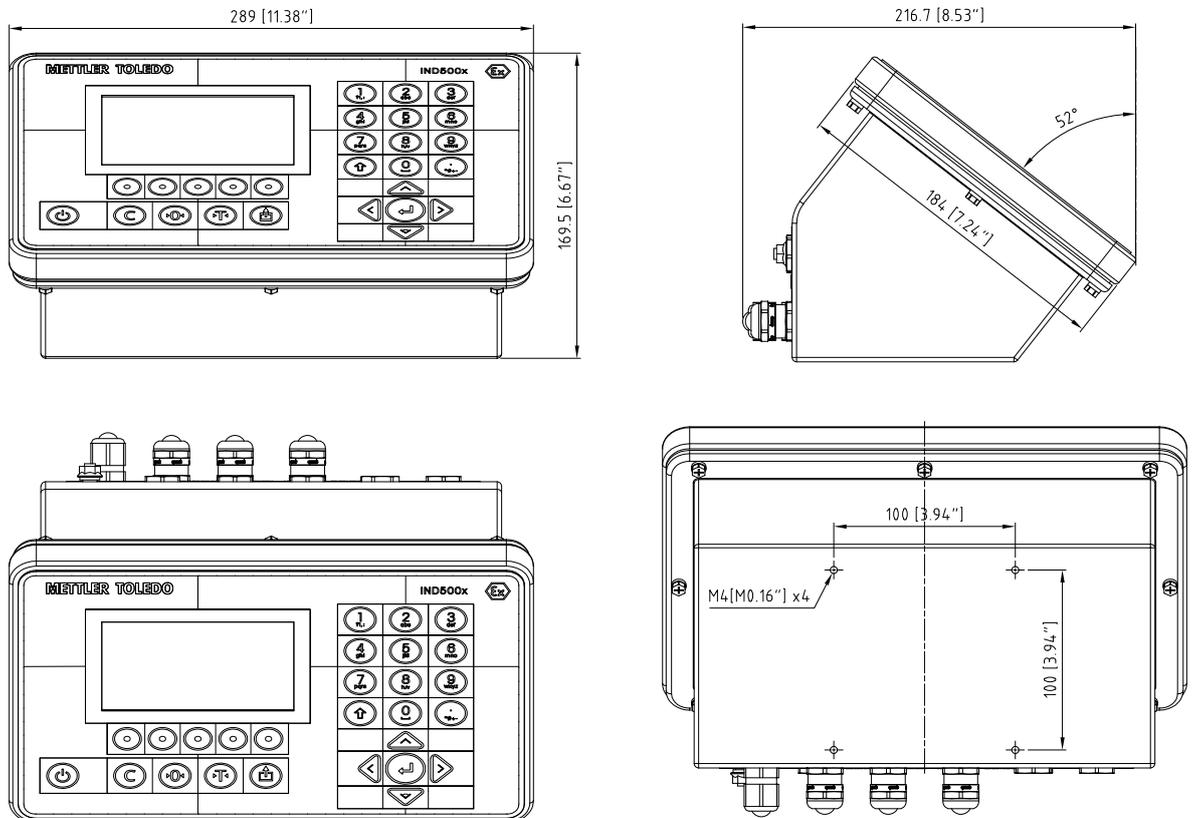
Abmessungen für IND500x Robust, Tischmontage
